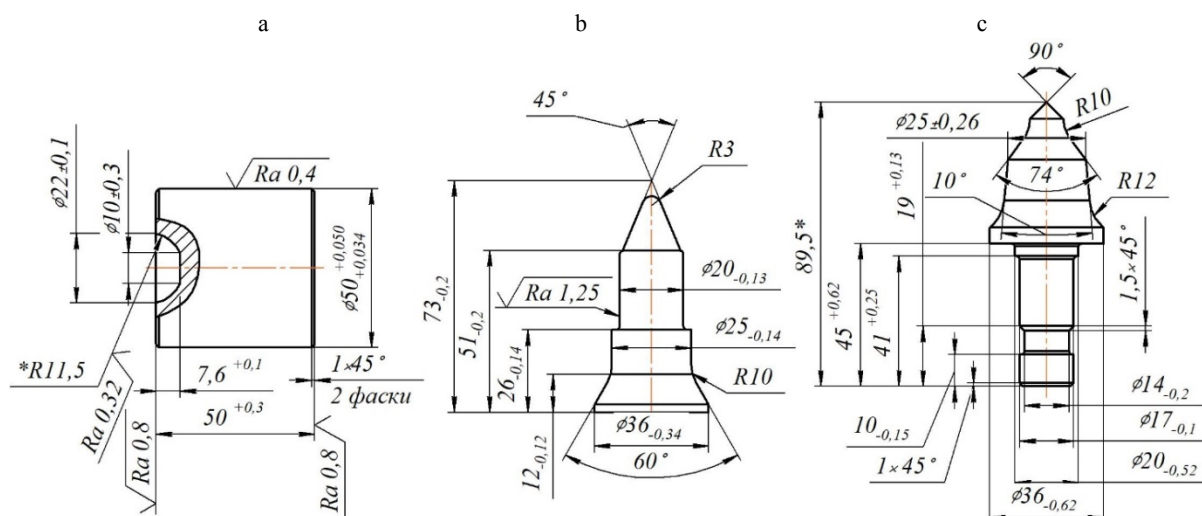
Детали-представители: а – вставка пуансона; б – прошивной пуансон; с – тангенциальный резец
